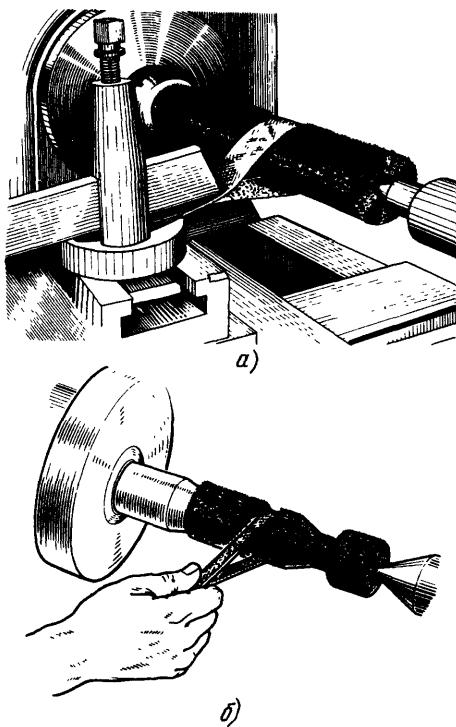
Обработка наружных поверхностей абразивной лентой:
